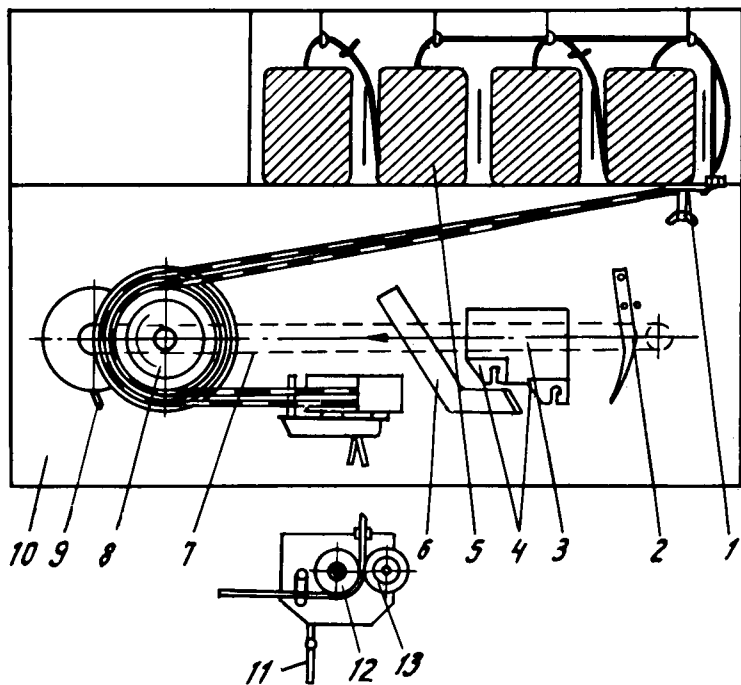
Обматывающий аппарат пресс-подборщика ПР-Ф-750: 1 - тормозок; 2 и 9 - ограничители; 3 - каретка; 4 - поводки; 5 - бобины; 6 - нож; 7 - цепной контур; 8 - механизм привода; 10 - рама; 11 - канат привода роликов; 12 - ролик; 13 - механизм подачи шпагата
